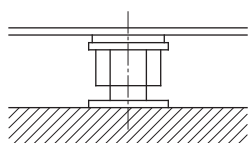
Нивелиращи болтове на повърхността на фундамента
